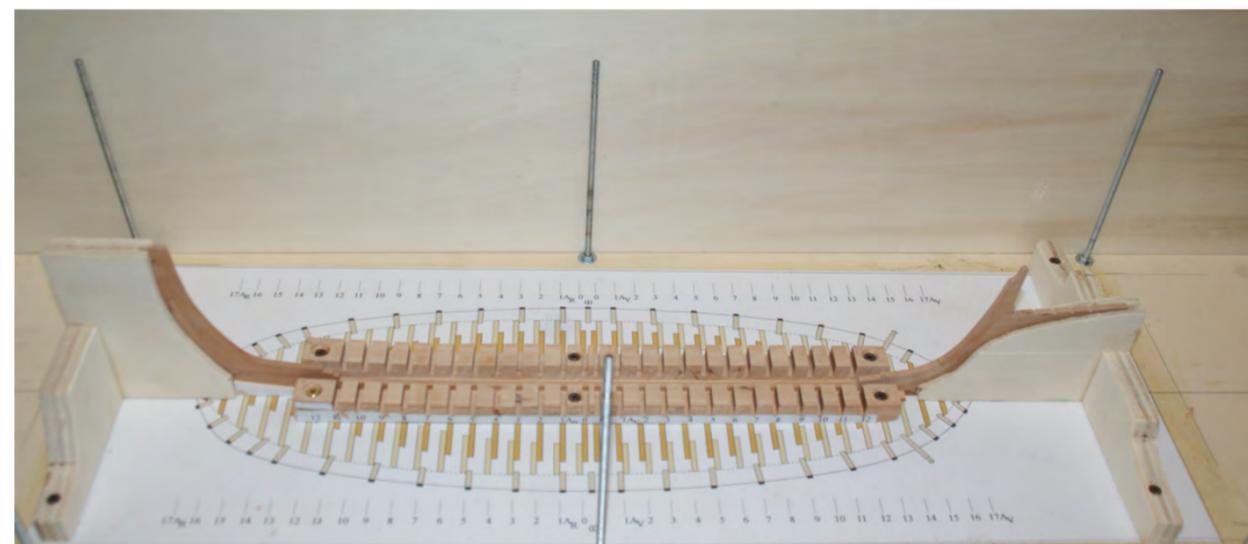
Pose de la quille sur la planche de travail prête à recevoir les couples. J'ai fixé à la verticale six tiges filetées de 6 mm sur ma planche afin de pouvoir loger la partie supérieure du chantier.
